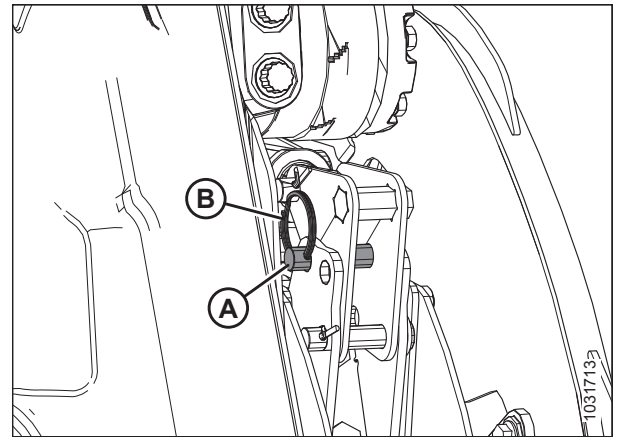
Cilindru brațului central stâng – poziția spre spate
